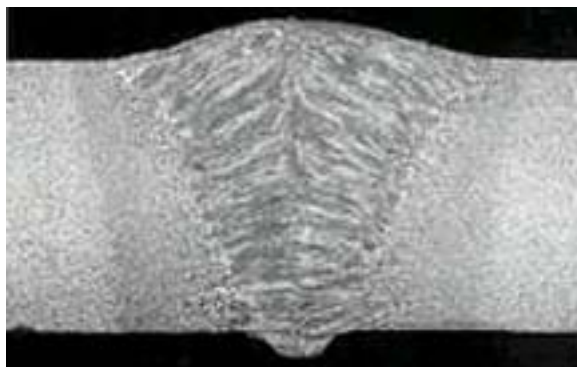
Шлиф сварного соединения из стали 10ХСНД, выполненного автоматической сваркой под слоем флюса при погонной энергии 1,9 кДж/мм
